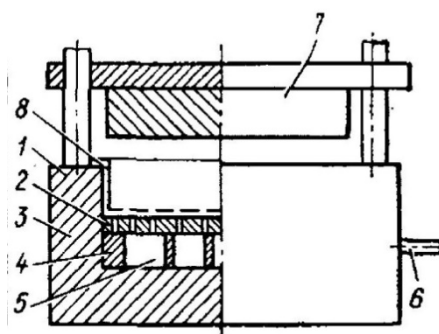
Установка, работающая под давлением для формования изделий плоской формы:
